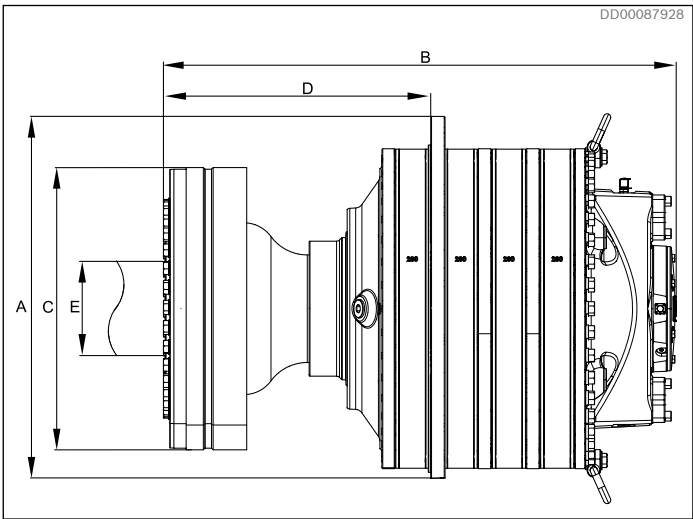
CB 1120 Motor mit Kupplungsadapter
